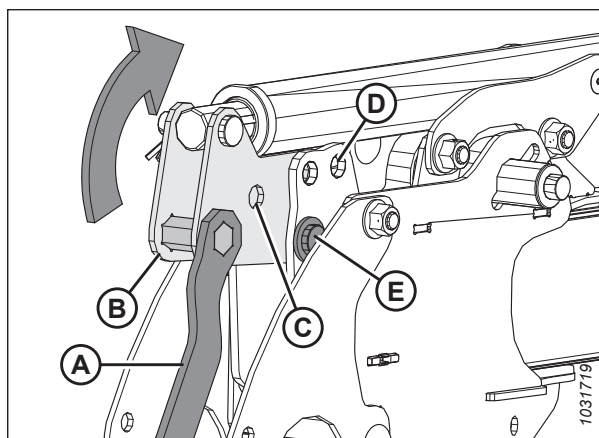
Réglage des vérins avant-arrière de type 1 – Position avant
